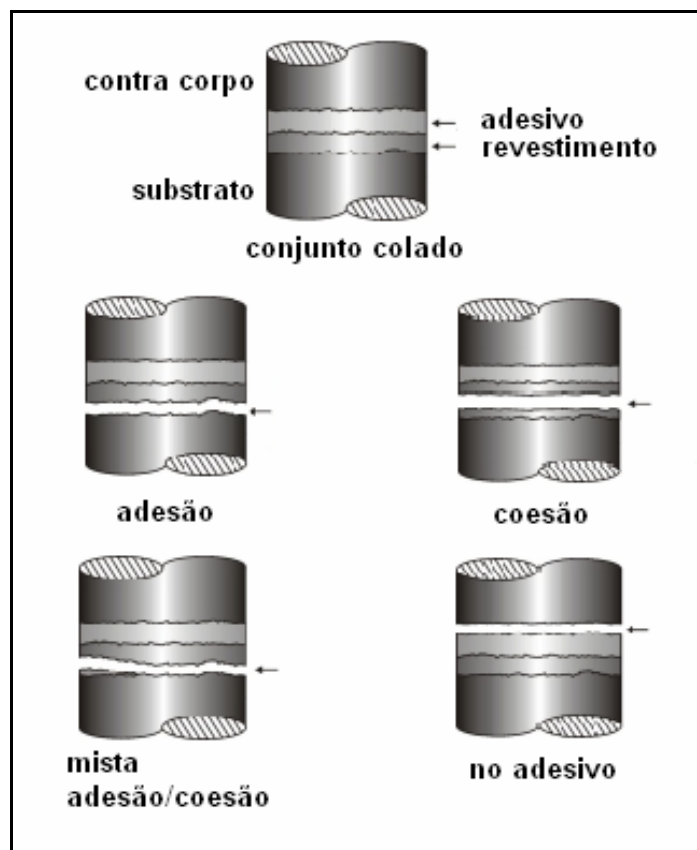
Tipos de falha do ensaio de aderência por tração. (adaptado da ref. 95)
